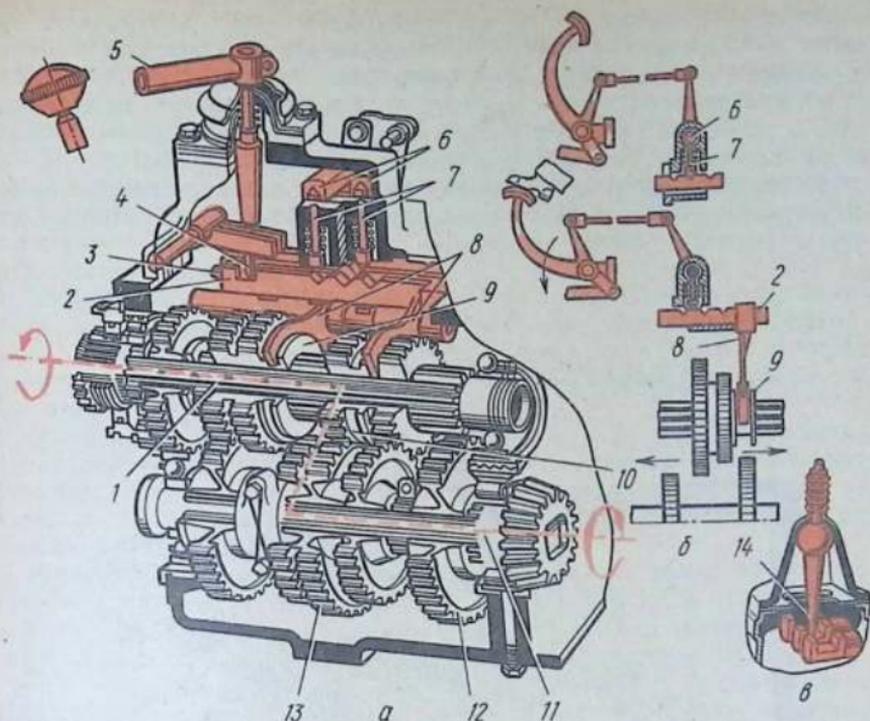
Коробка передач трактора ДТ-75 МВ:
